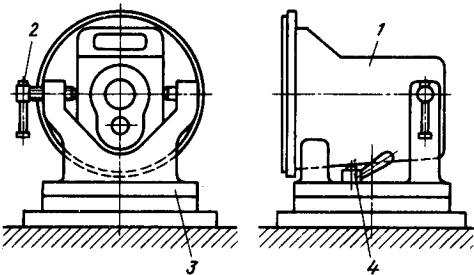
Сборочное приспособление с вертикальной осью поворота
